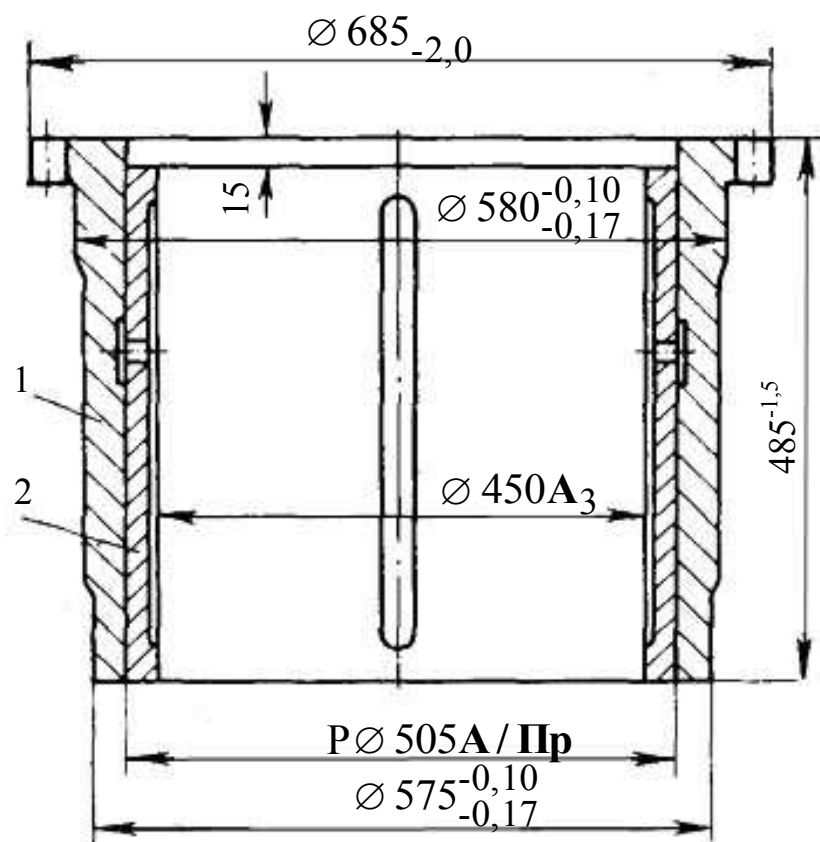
Ремонтный чертеж центральной отливки в сборе:
